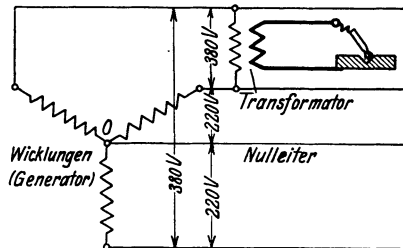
Drehstromsystem in Sternschaltung mit Schweißtransformator zwischen zwei Phasen.
